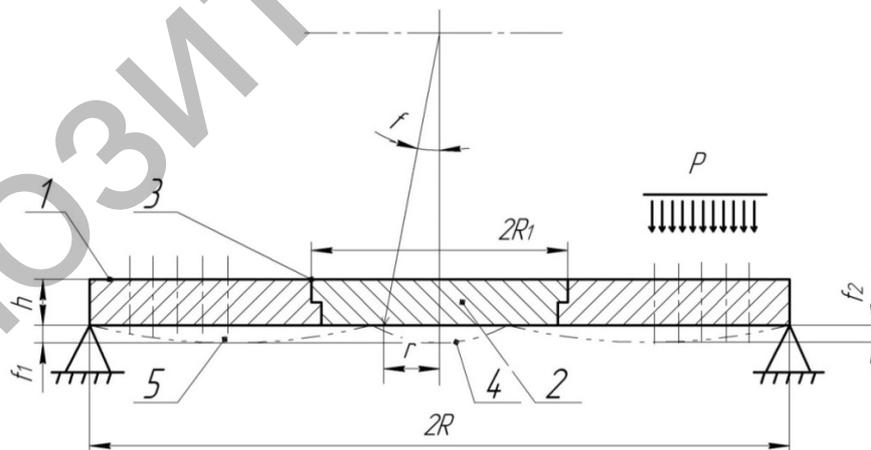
Схема деформаций корпуса составной матрицы с шарнирным креплением по наружному контуру
